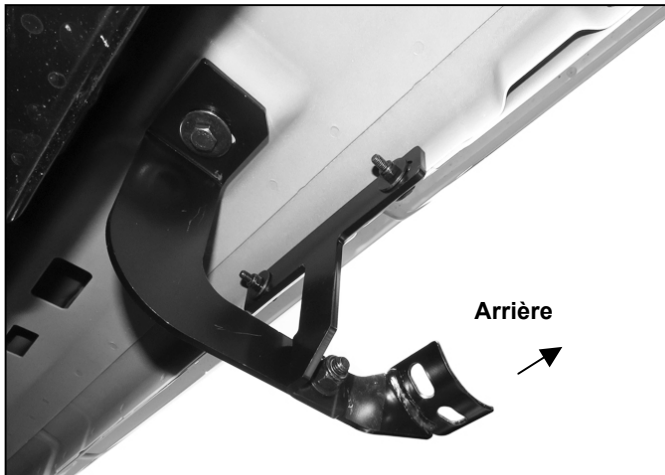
Fixer la barre de fixation avant à l'arrière du joint de soudure
